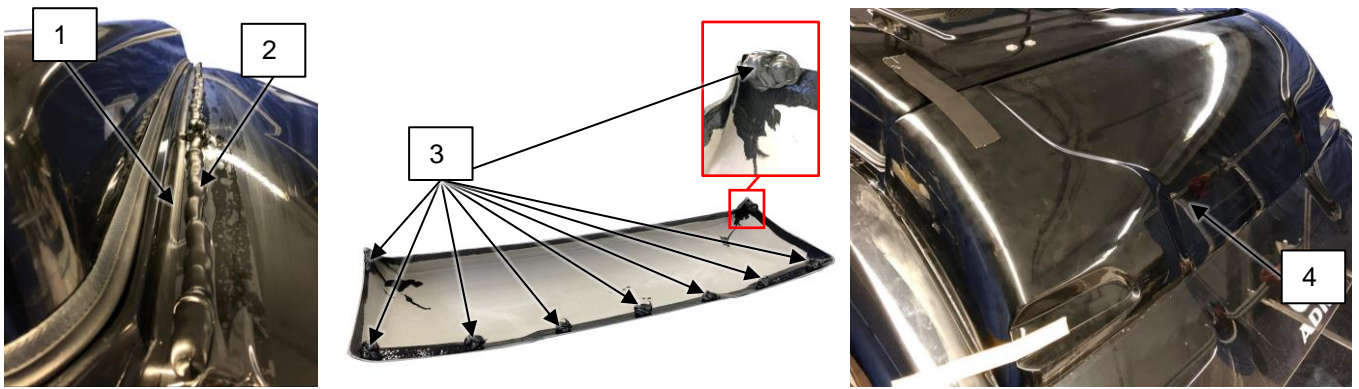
Montage des Frontspoilers / Installation of the front spoiler
